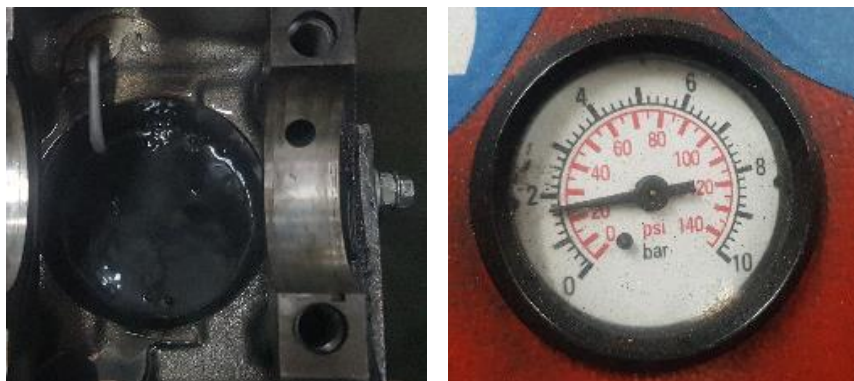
Fuga pela camisa do cilindro #1 e pressão de ensaio da ordem dos 2 bar.
